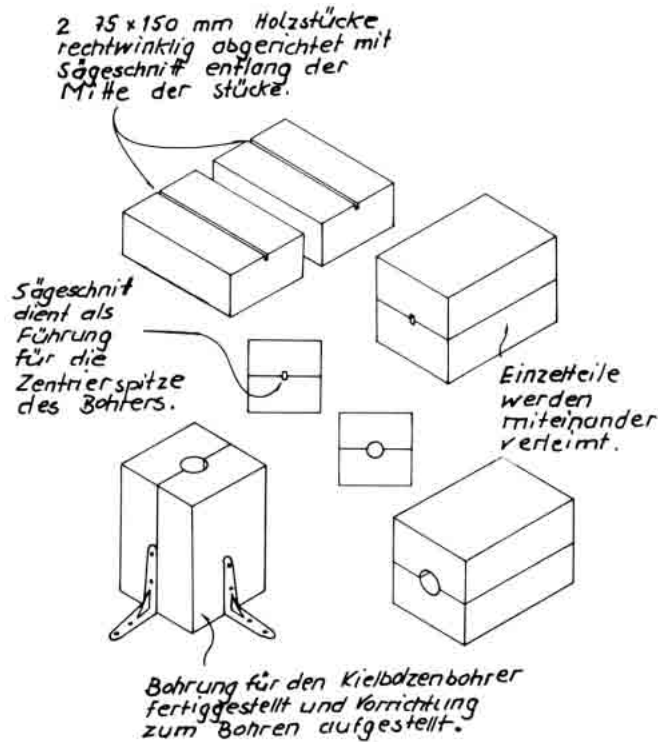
Vorrichtung zum Bohren der Löcher für die Kielbolzen.
